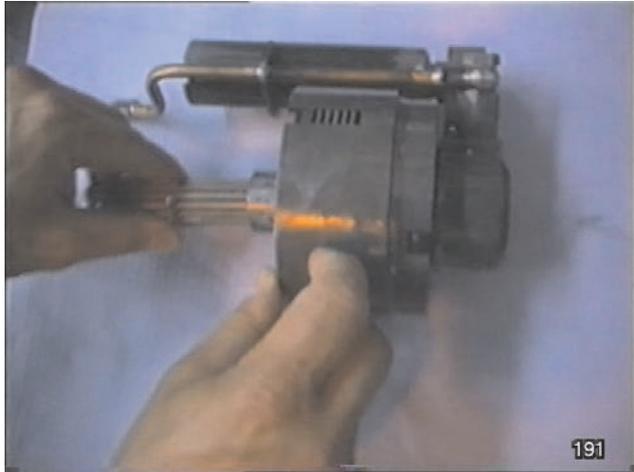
Dégager l'arbre avant de l'ensemble embrayage.
